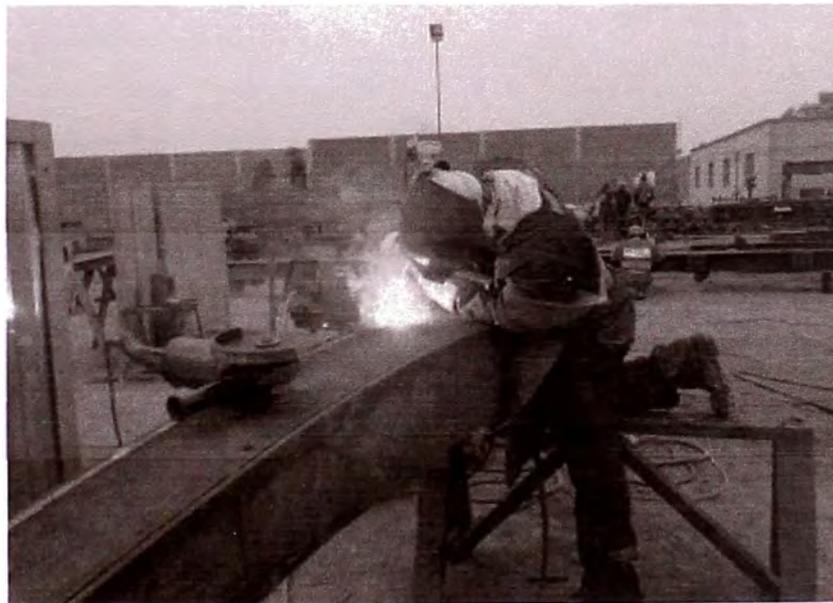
Soldadura en columnas con proceso GMAW
